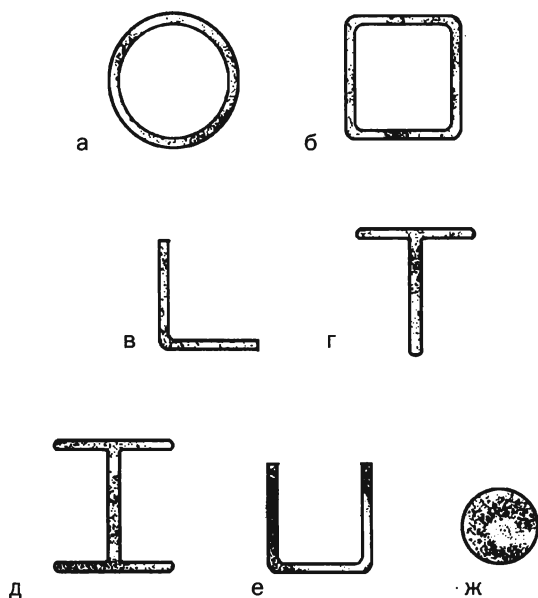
Разновидности металлического профиля: а — труба; б — квадрат; в — уголок; г — тавровый профиль; д — двутавровый профиль; е — швеллер; ж — пруток
